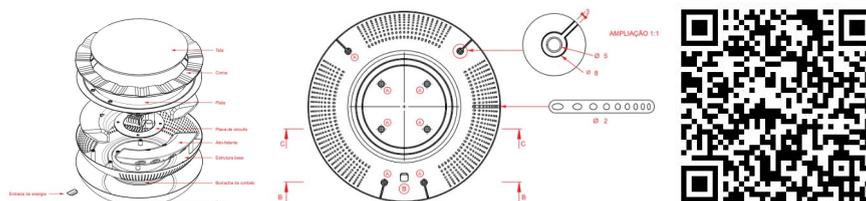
Parte do desenho técnico e QR Code com o arquivo.
